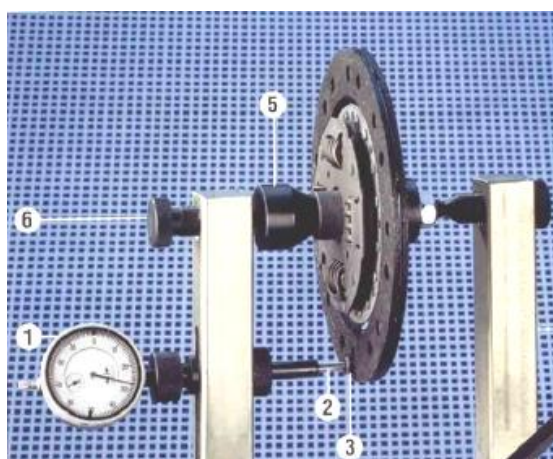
Проверка биения рабочей поверхности ведомого диска.
